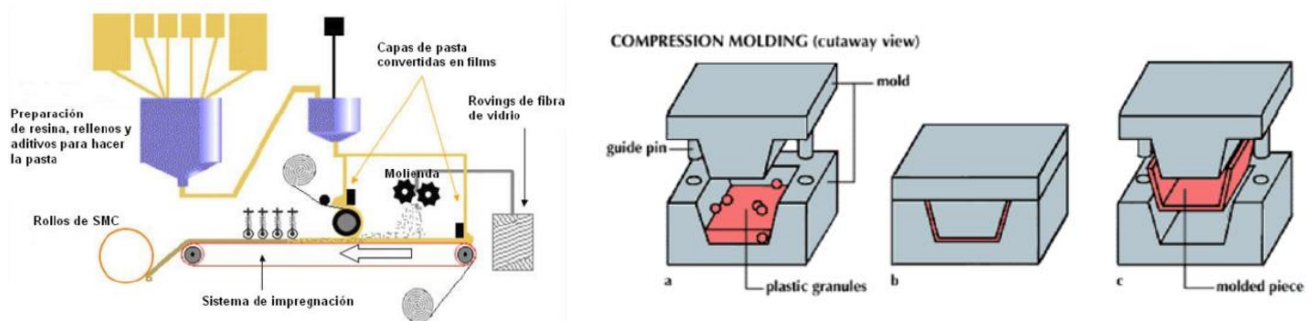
Figura E: Proceso de fabricación de “Sheet moulding compound” – SMC. A la izquierda fabricación de SMC y derecha proceso de moldeo (Compression Molding)
